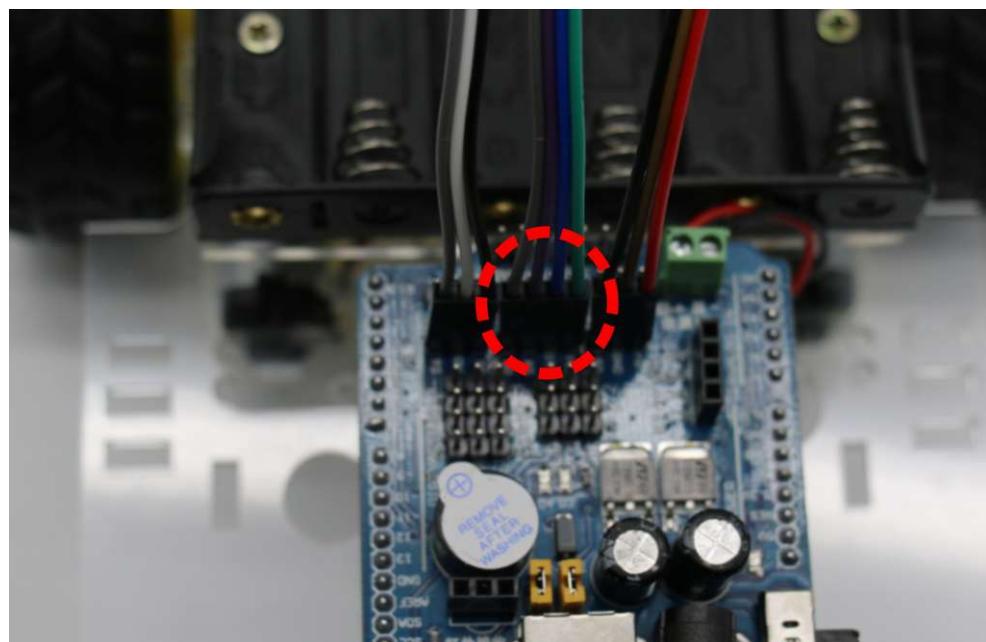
4. Vista del otro extremo de los cables enchufado al módulo Shield.
